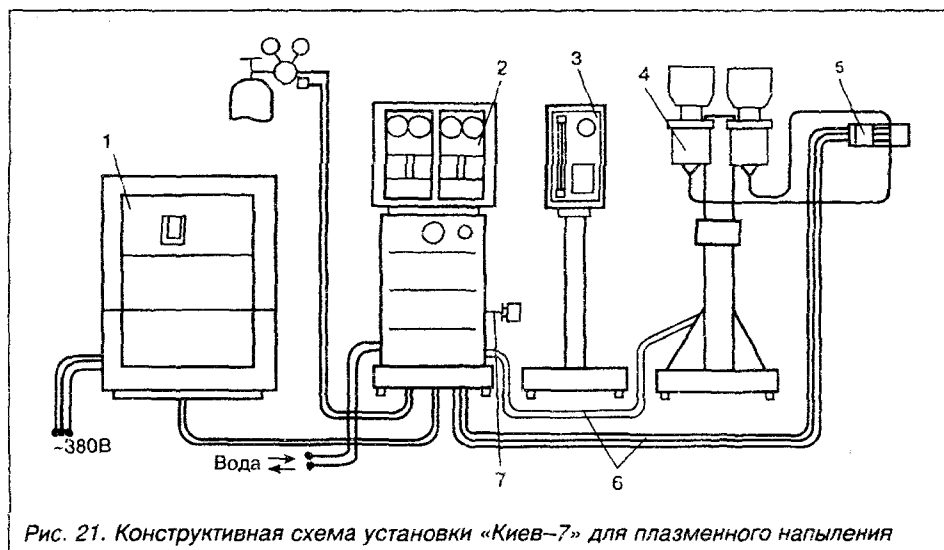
Конструктивная схема установки «Киев-7» для плазменного напыления
